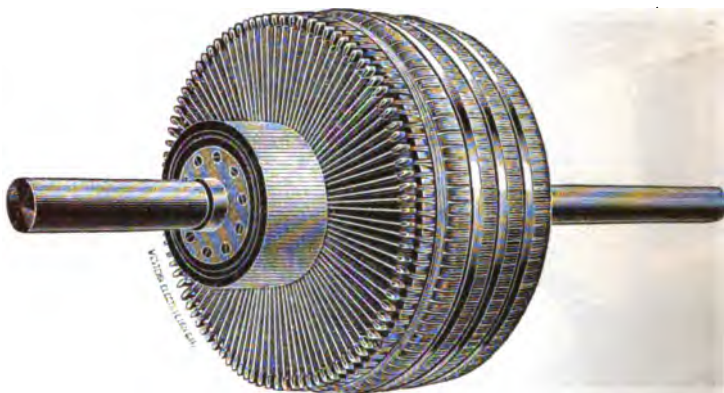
Anneau de la machine Sperry (Electric Company, Chicago).
